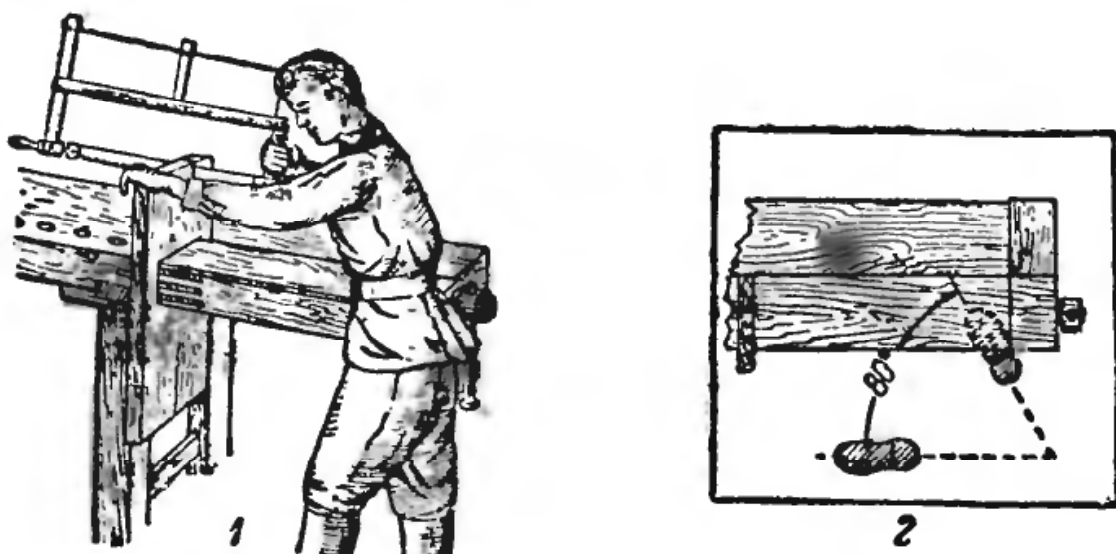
Пиление „в торец“: 1 — общий вид рабочего места; 2 — положение в плане.
